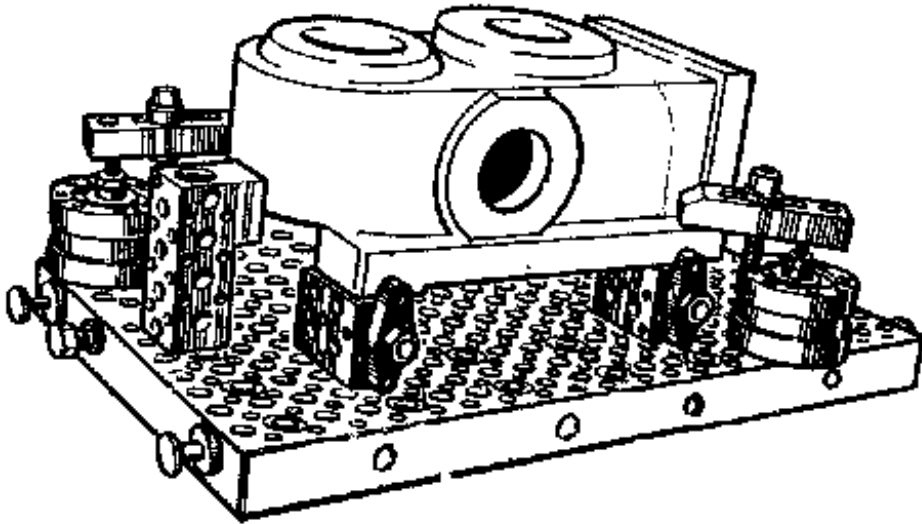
Компоновка УСПО с вертикальными гидроцилиндрами
